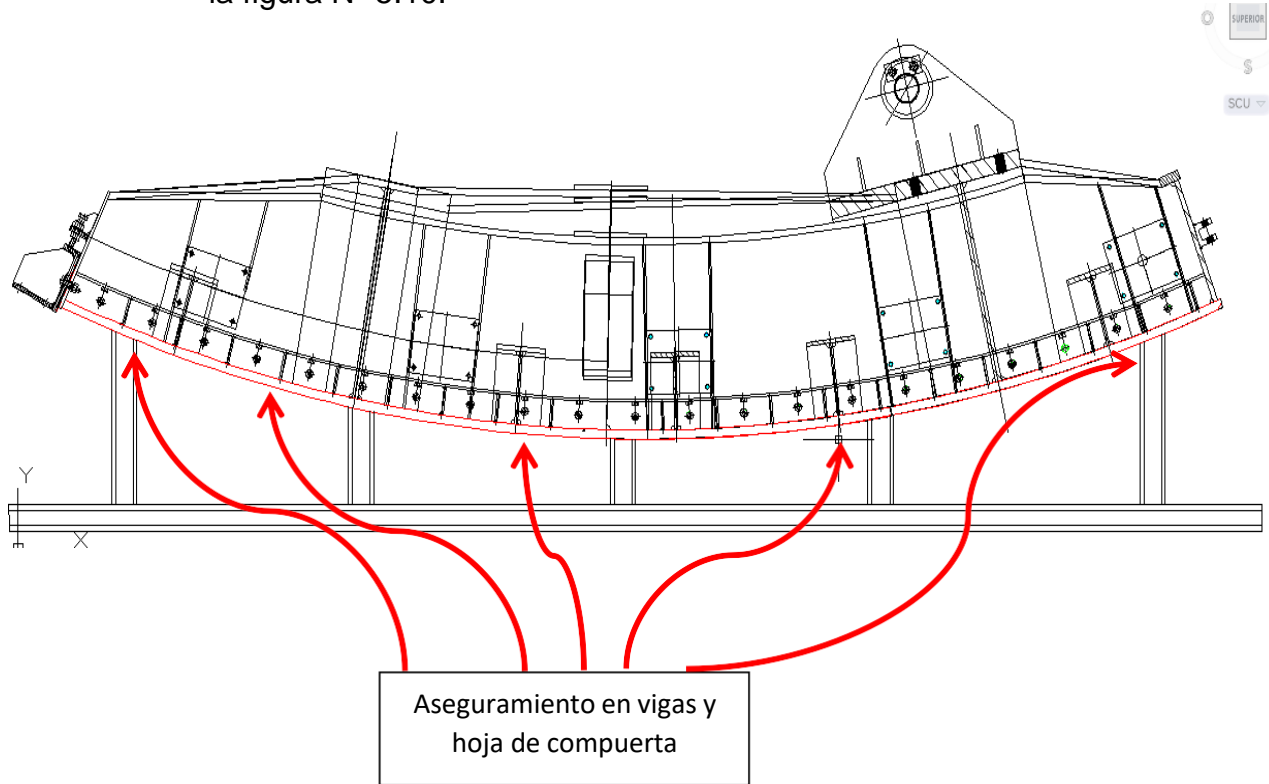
Soldeo de aseguramiento en vigas y hoja de compuerta. Fuente: Propia
